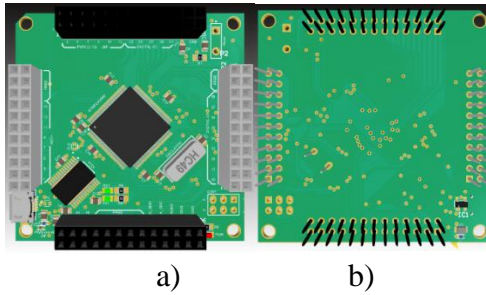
Layout placa de bază TOP a), BOT b)
